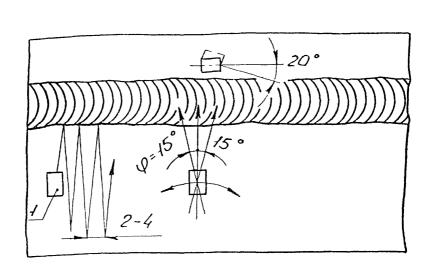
Схемы прозвучивания сварных соединений
